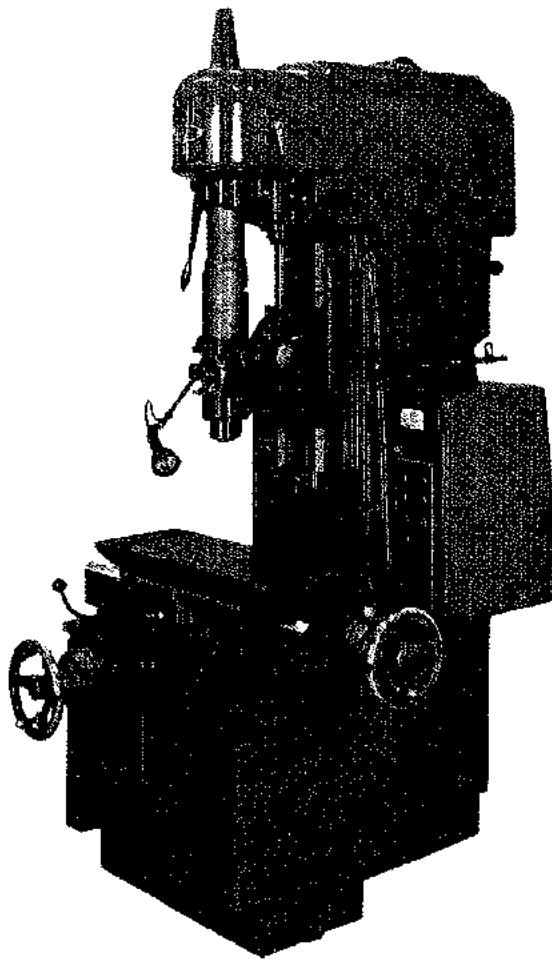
Máquina de precisión para plantillas de agujeros (Moore Special Tool Co., Inc.)
